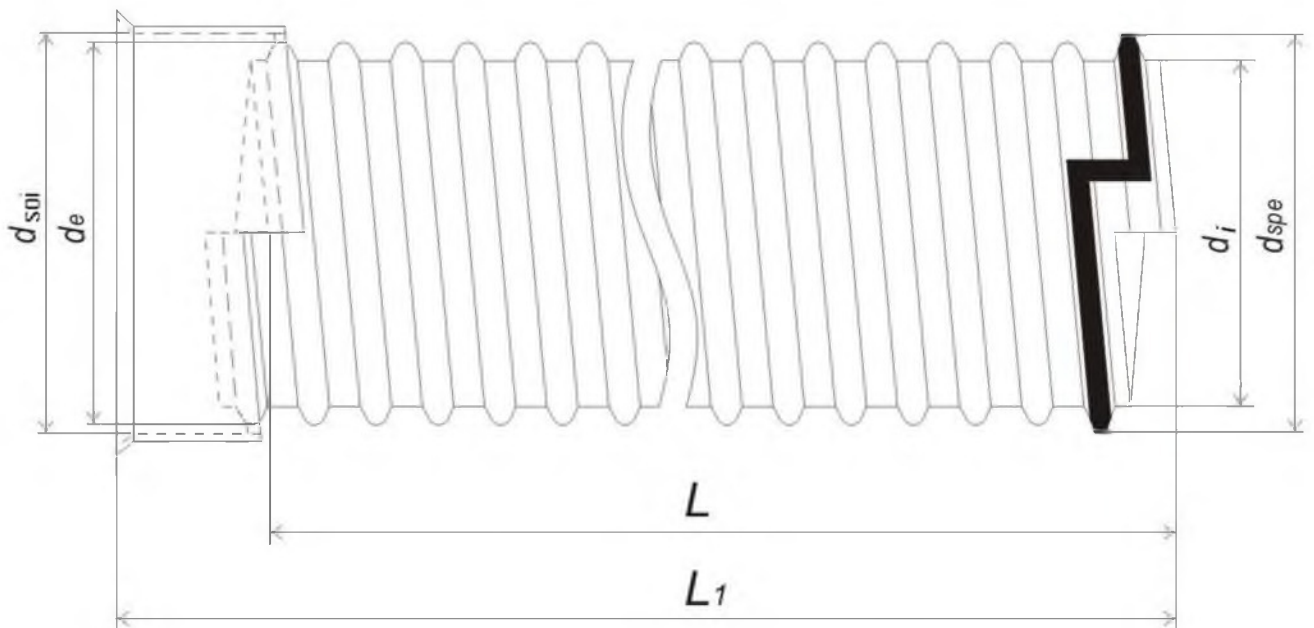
Конструкция труб с раструбным соединением с помощью уплотнительного кольца
